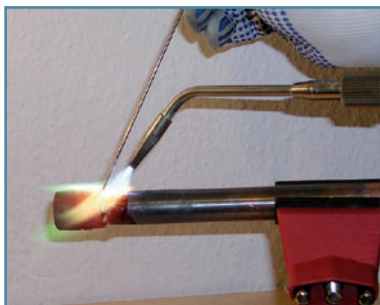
Soldadura fuerte de adaptador de latón
